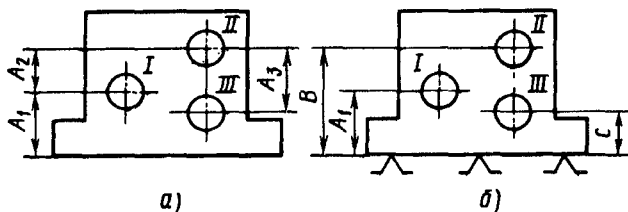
Схемы простановки координатных размеров отверстий корпусной детали в вертикальной плоскости при использовании принципа:
